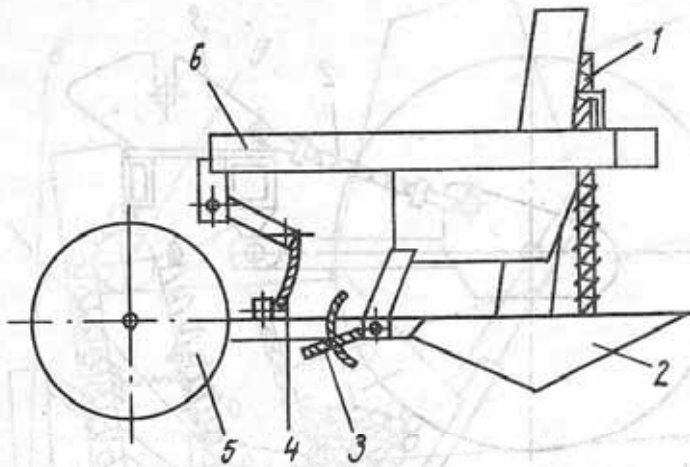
Подвеска сошниковой группы: 1 - нажимной механизм; 2 - сошник; 3 - регулировочный механизм; 4 - цепочка подвески; 5 - диск; 6 - рама
